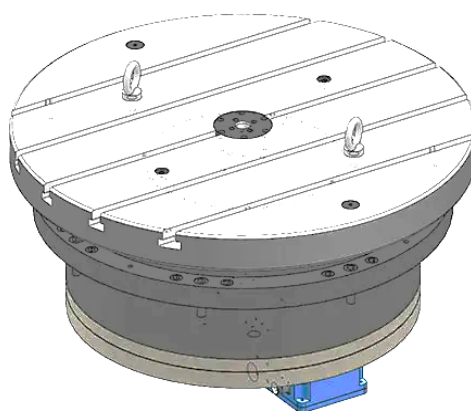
Вертикальный поворотный стол с компактным редуктором
